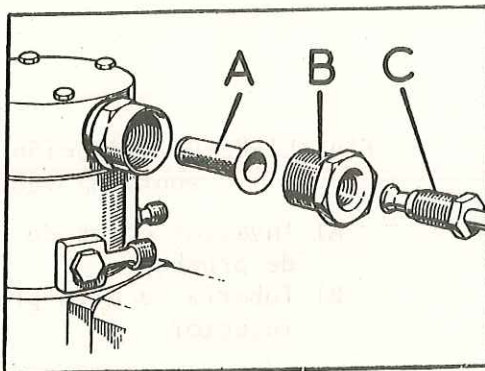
Limpieza del filtro de entrada de la bomba inyectora
